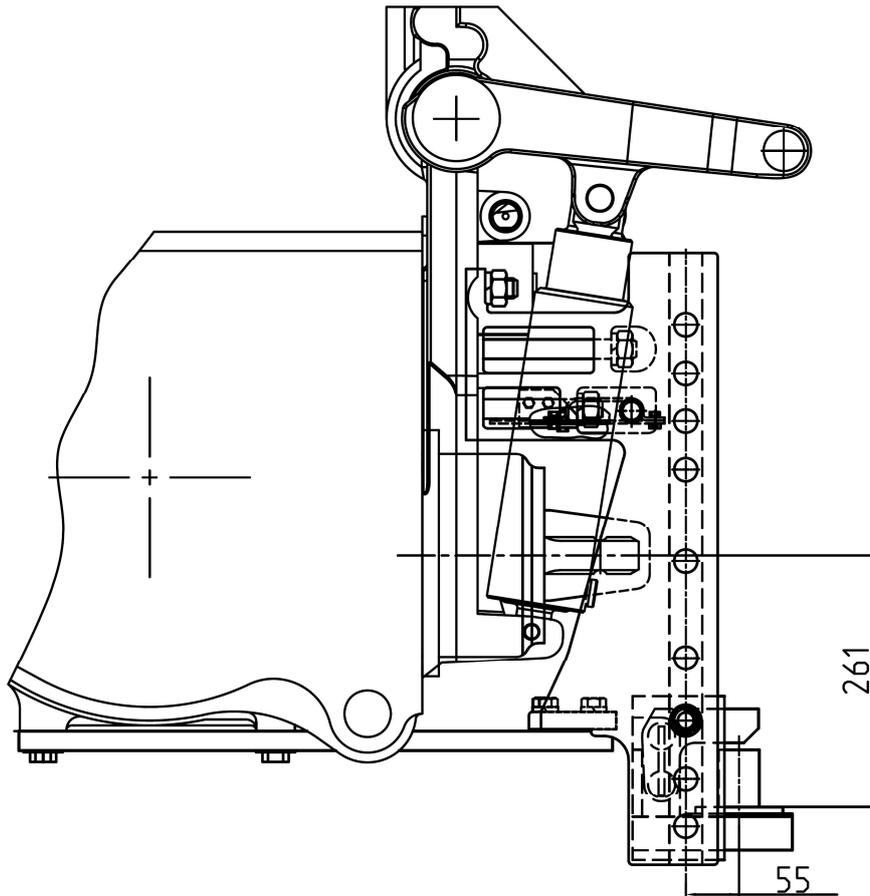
Schéma des variantes d'installation du dispositif TSU-2R (dispositif de traction "python")
